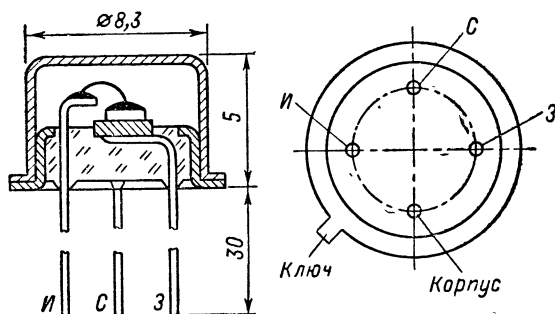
Крепление кристалла в корпусе и цолевка 2П302.
